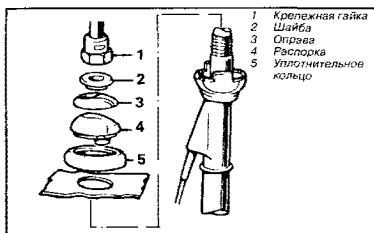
Правильный порядок установки набора деталей крепежа антенны
